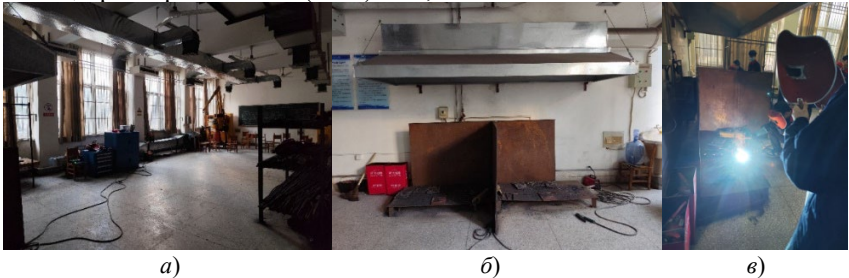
Место проведения натурных исследований характеристик сварочного аэрозоля: *а* – общий вид сварочного цеха; *б* – вид сварочного поста; *в* – процесс сварки
